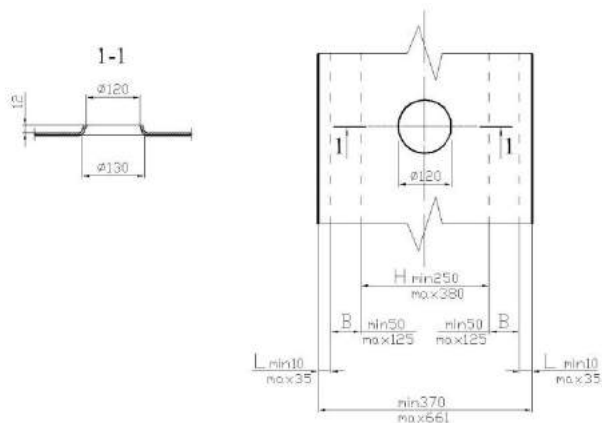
Схема расположения технологических отверстий в исходной заготовке профиля.
